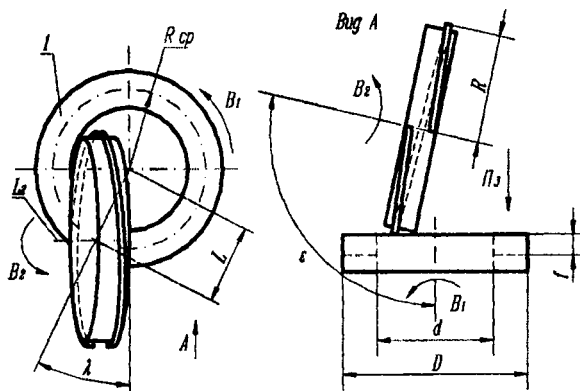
Схема формообразования прерывистых поверхностей червячным инструментом
